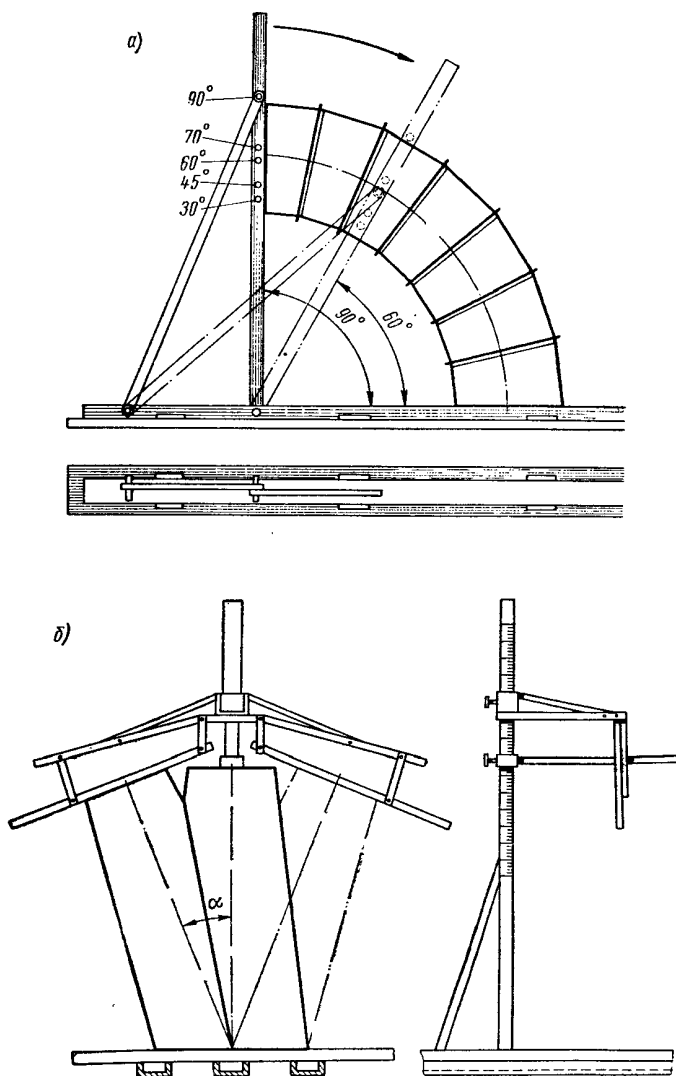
Приспособления для проверки углов и размеров фасонных частей
